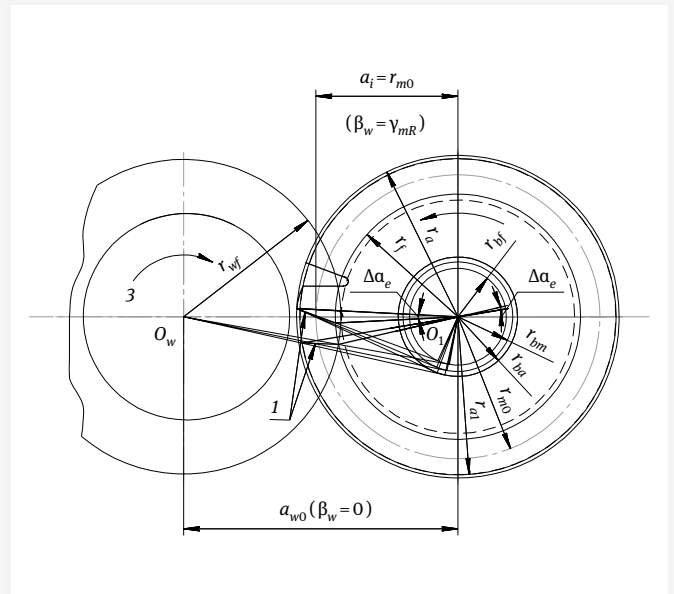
Формирование линий контакта при шлифовании поверхности с прямолинейным профилем: 1 – линии контакта прямолинейного профиля, 2, 3 – направления вращения фрезы шлифовального круга
